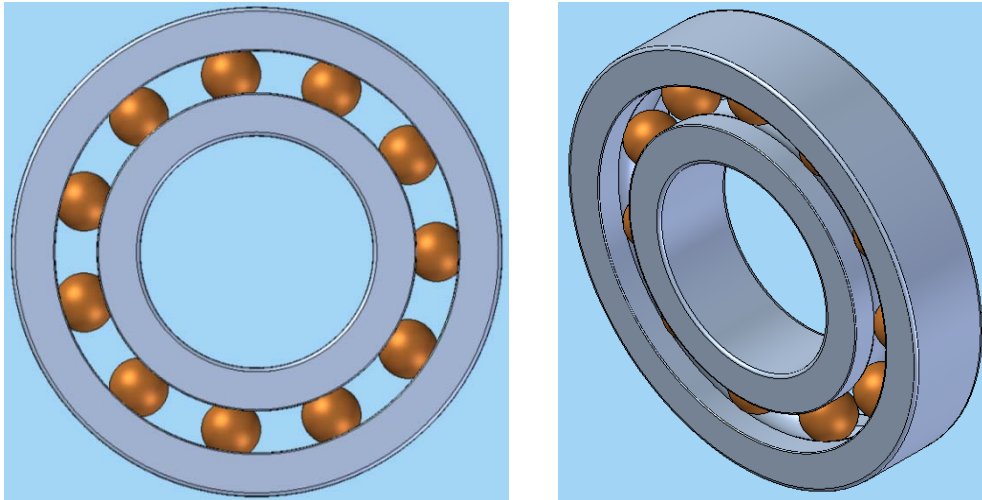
Vista frontal e isométrica del rodamiento elegido.
